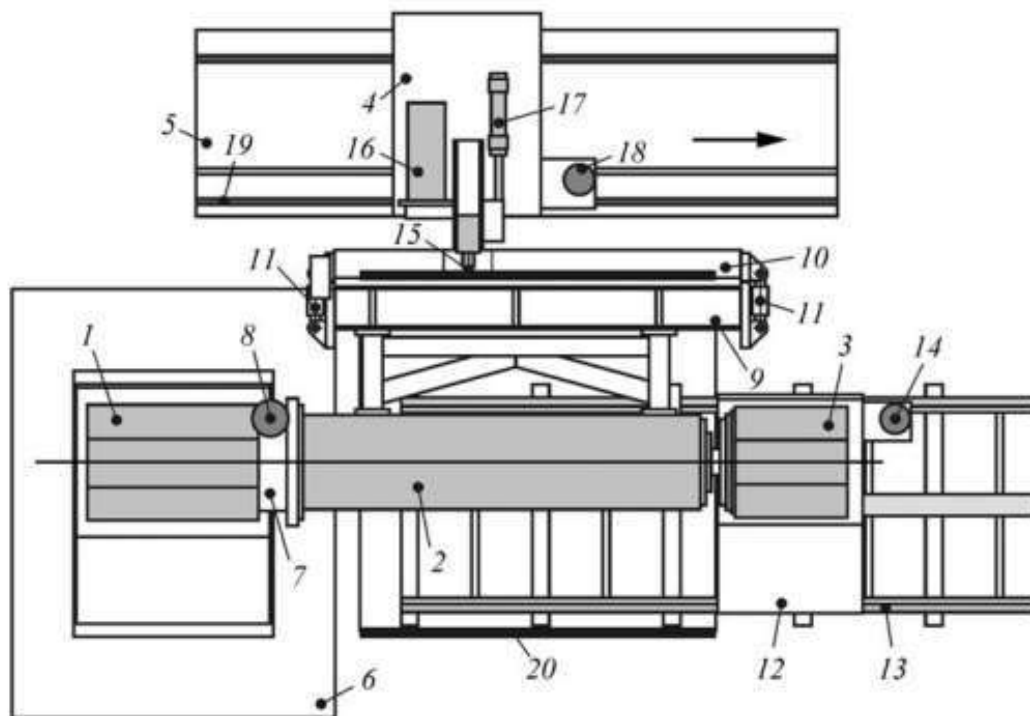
Станція зварювання тертям з перемішуванням при зварюванні поздовжнього шва
